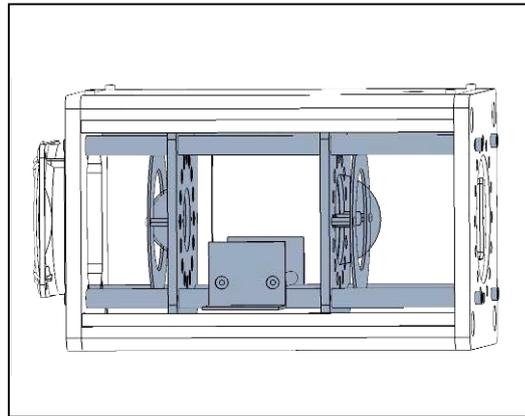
Blick in den seitlich geöffneten Lampenkasten. Hinter der Trägerkonstruktion für das Leuchtmittel sitzt der Kugelspiegel (links) davor eine asphärische Sammellinse (rechts) um das Licht zu bündeln..
